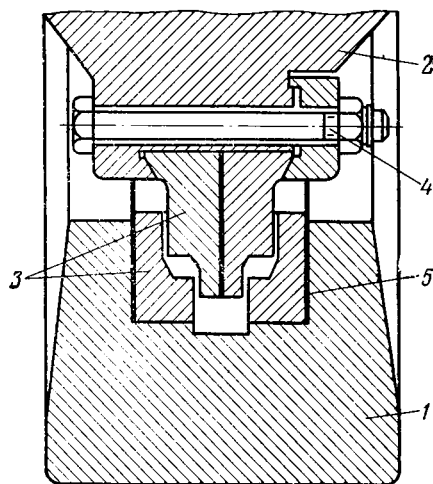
Схема установки формовочных деталей кольцевого пресса:
